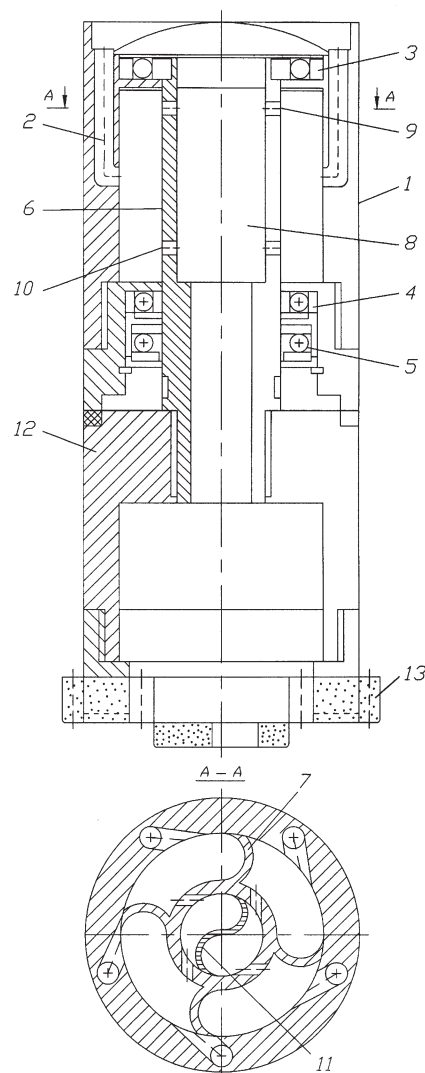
Общий вид двухкамерной забойной гидромашин с самовращающимся долотом: 1 — корпус гидромашин; 2 — подводящие каналы; 3–5 — подшипники; 6 — вал; 7 — лопасти; 8 — центральный канал; 9 — верхние боковые радиальные отверстия; 10 — нижние боковые радиальные отверстия; 11 — синусоидальная перегородка; 12 — переходник; 13 — ступенчатое долото
